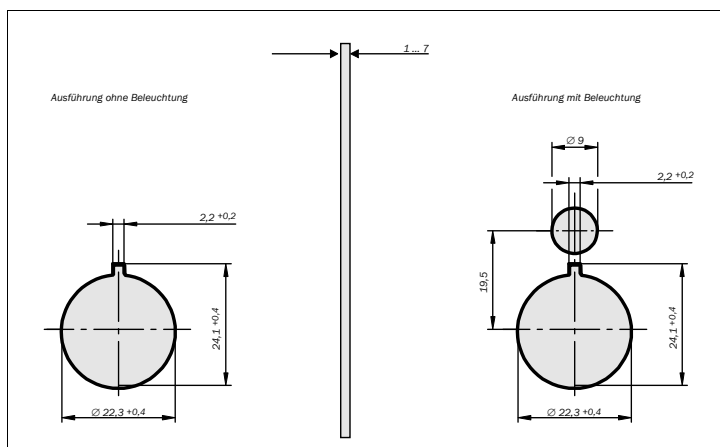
Maßbilder der Montagelöcher für die Einbauversionen (mm)
